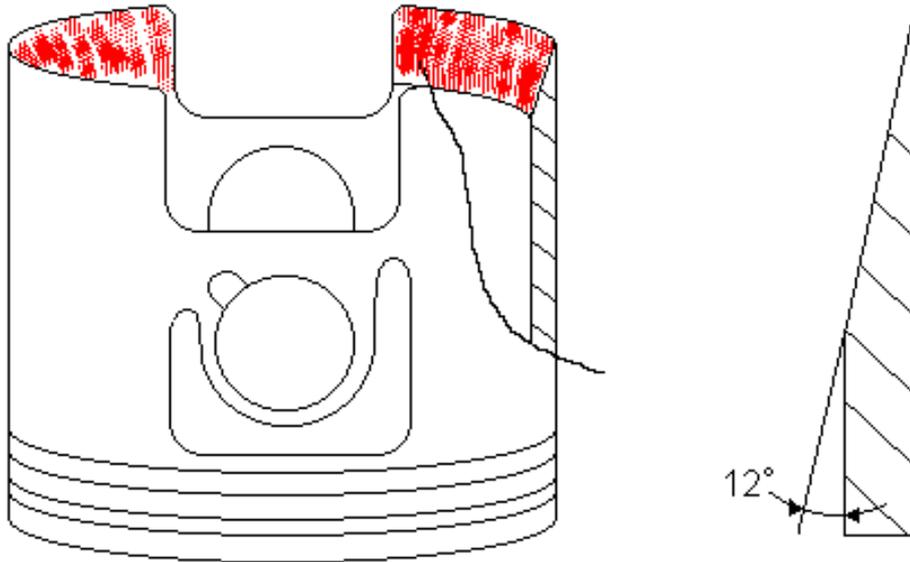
Kolbenbearbeitung am Kolbenhemd
